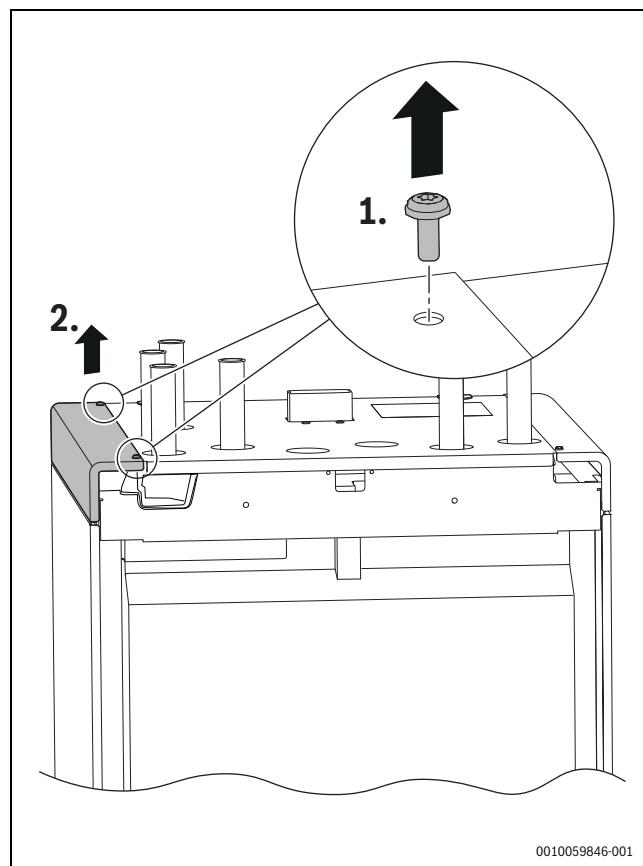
Rückansicht: Ecken mit Befestigungsschrauben
